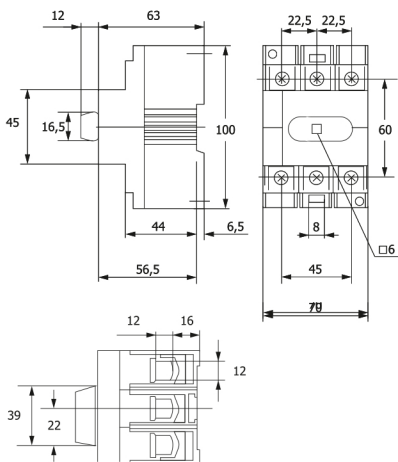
Габаритные и установочные размеры рубильников 40-100А
